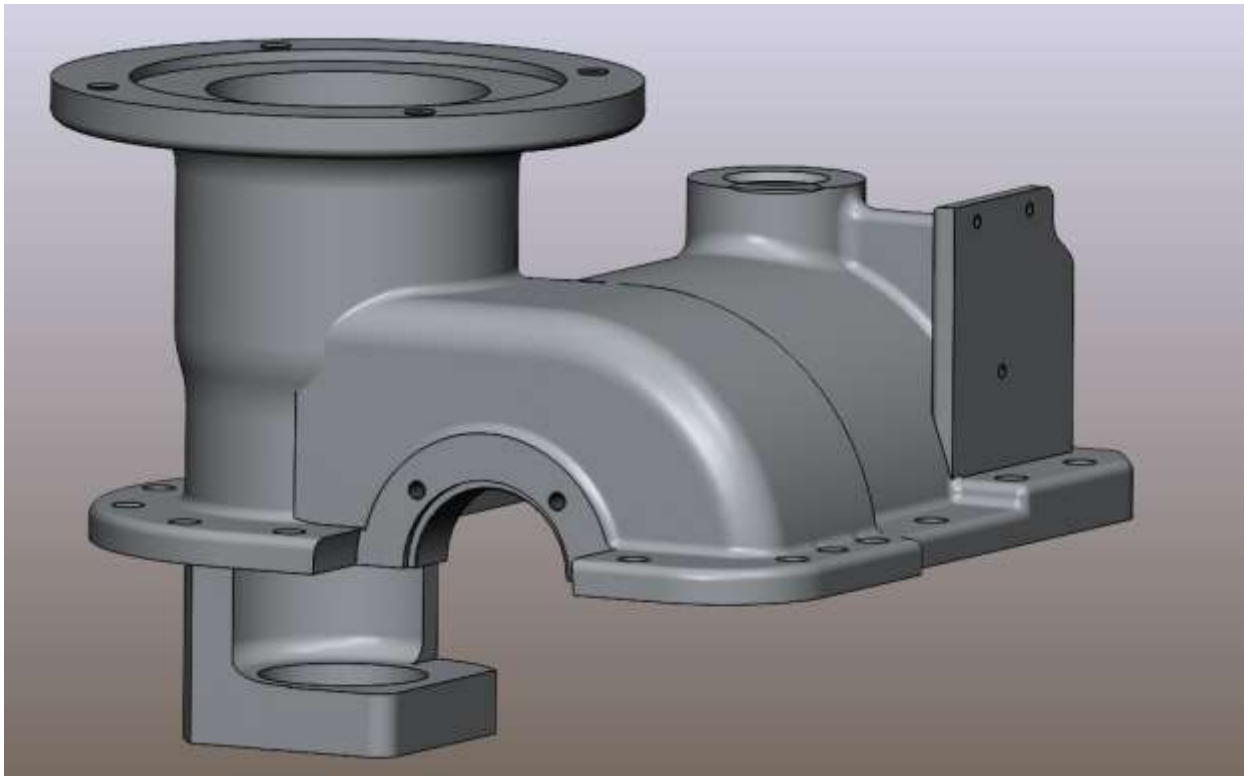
3D-модель деталі «Корпус валоповоротного пристрою»
